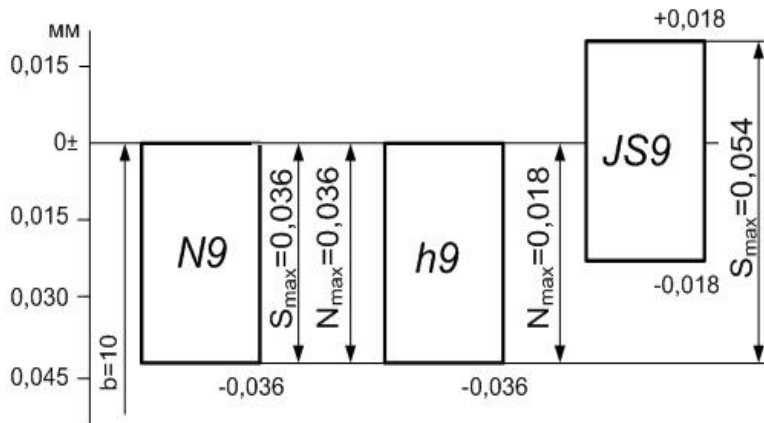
Схема розташування полів допусків шпонкового з'єднання
